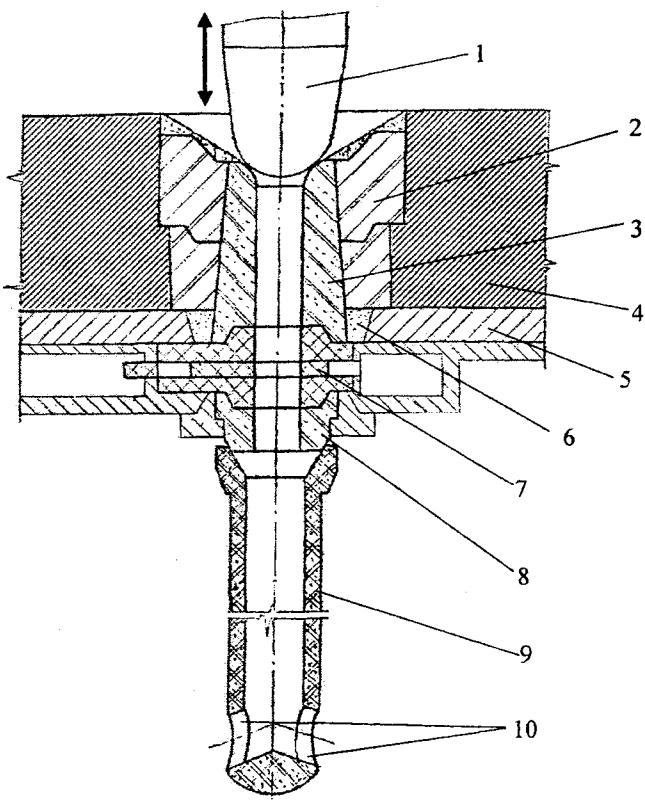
Схема разливочного узла промежуточного ковша со стопорным устройством слябовой МНЛЗ:
